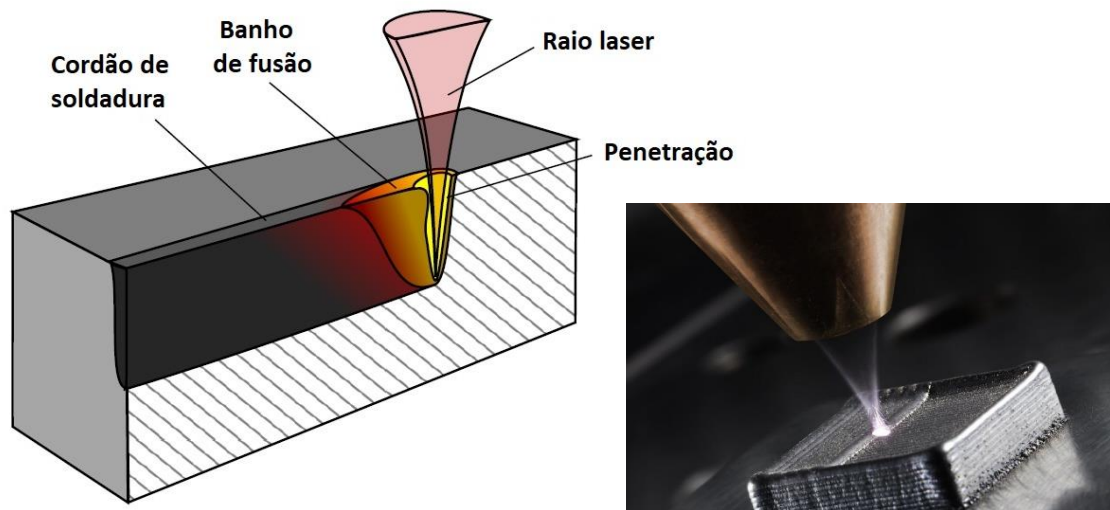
Soldadura Laser [Adaptado de (IONIX, LASER WELDING, s.d.)].
